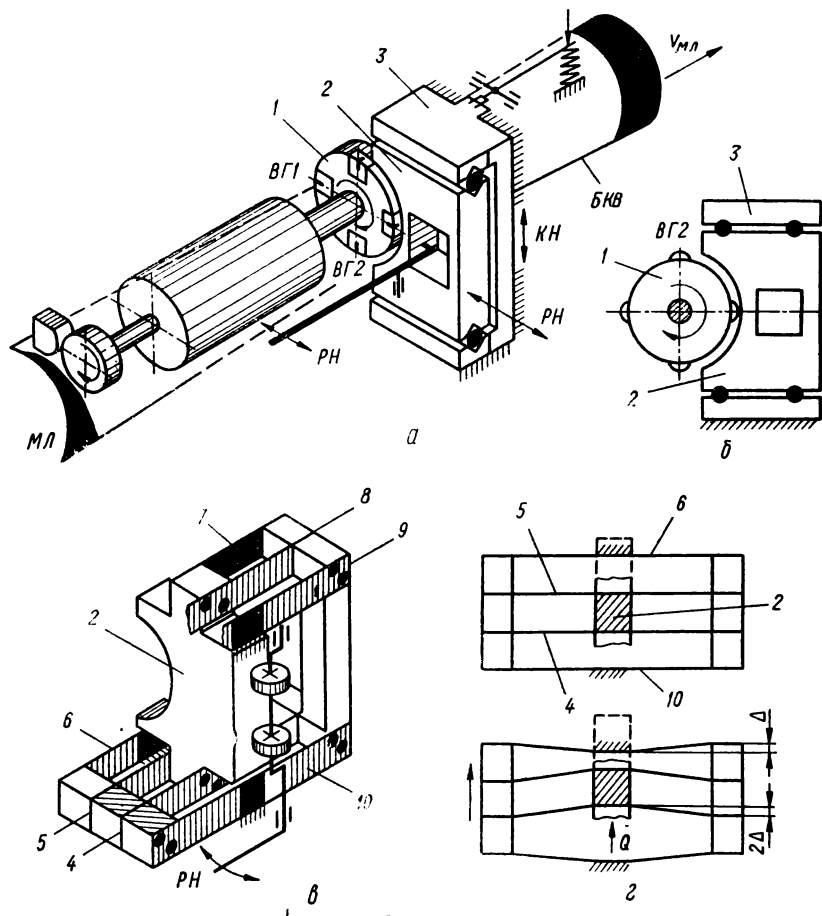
Кинематические схемы БВГ ПСЗ с прямолинейным движением направляющей камеры
